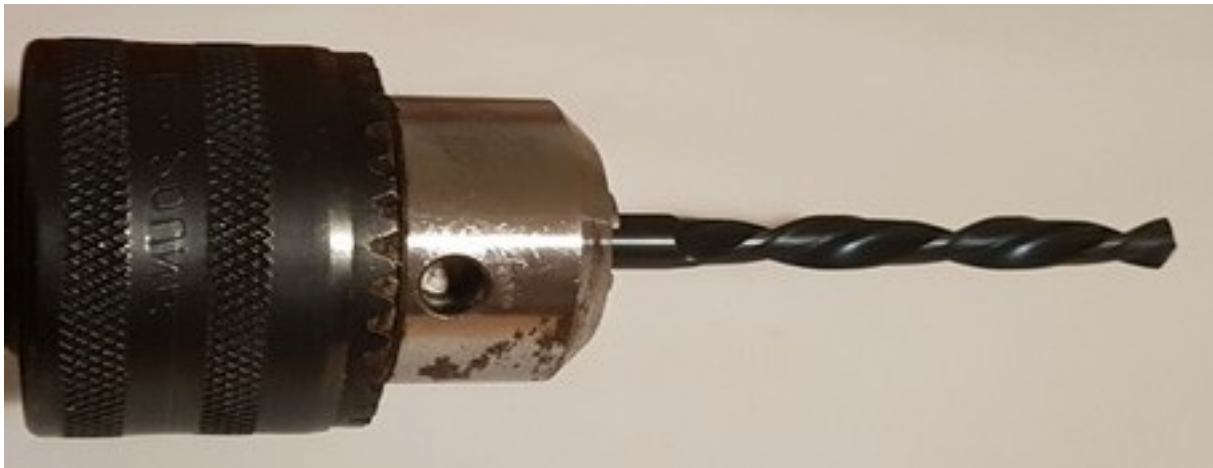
Bohrfutter mit Werkzeug einer Bohrmaschine
